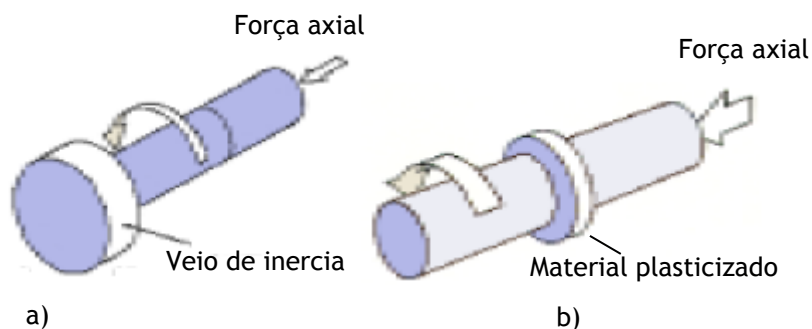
Soldadura por fricção rotacional: a) inércia; b) contínua
